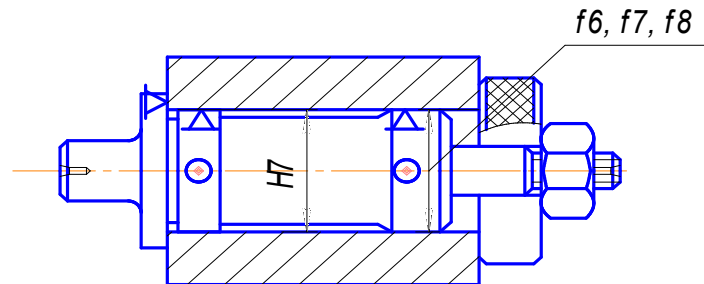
Цилиндрическая оправка для посадки заготовок с зазором
